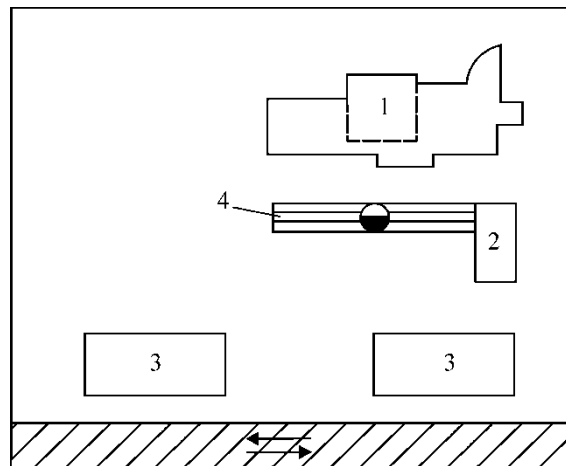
Робоче місце токаря (площа 23,2 м²): 1 – токарно-гвинторізний верстат; 2 – тумбочка для інструменту; 3 – стелаж для деталей; 4 – підставка-решітка.
